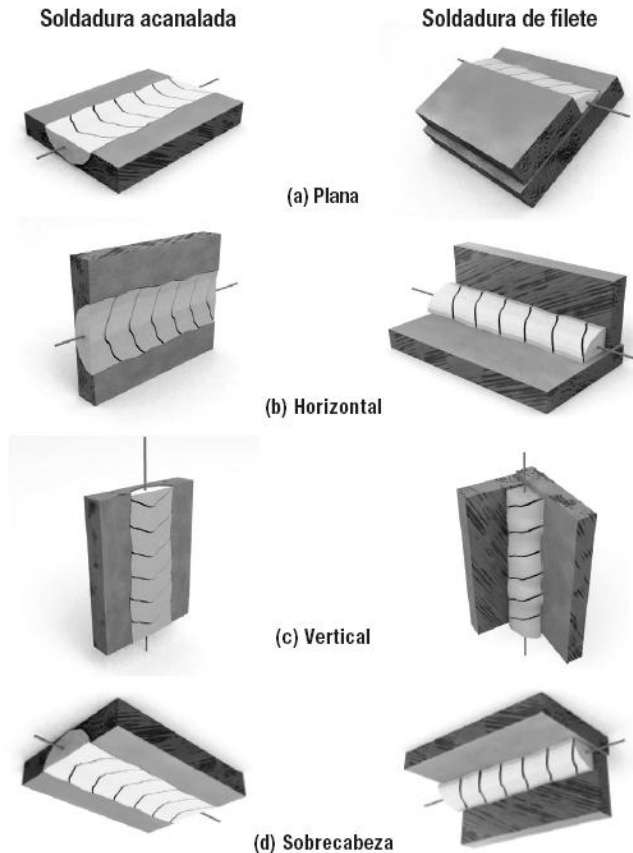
Diferentes configuraciones de la posición del electrodo al soldar.
